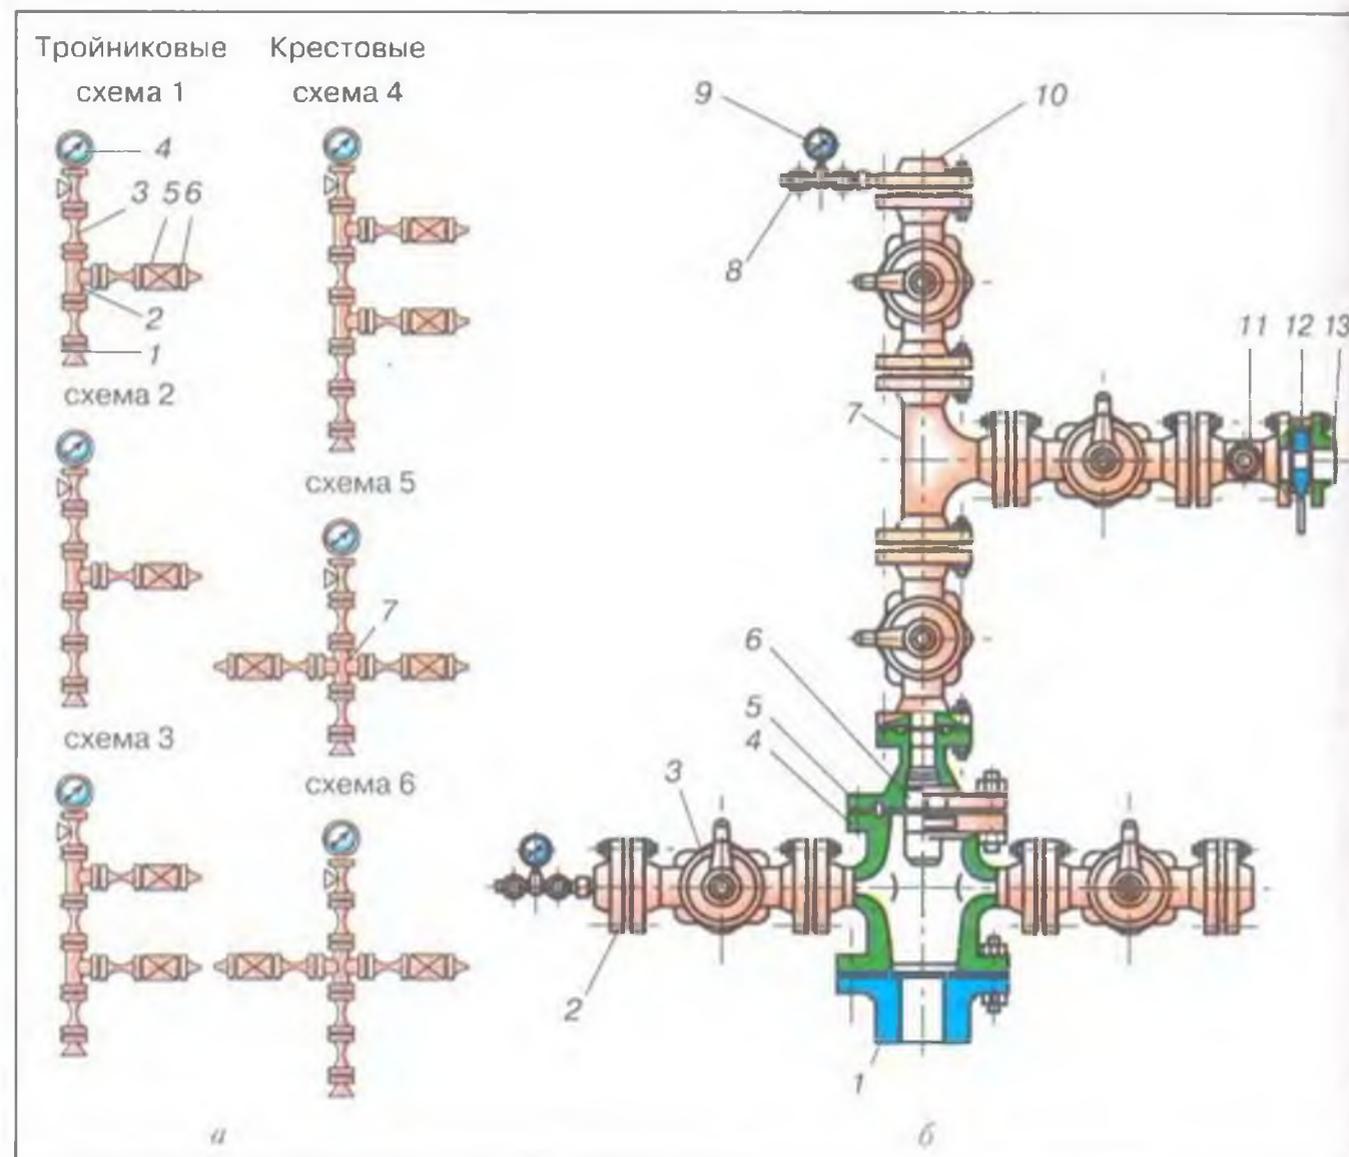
Устьевое оборудование: а – типовые схемы фонтанных елок (1 – переводник к трубной головке; 2 – тройник; 3 – запорное устройство; 4 – манометр с запорно-разрядным устройством; 5 – дроссель; 6 – ответный фланец; 7 – крестовина); б – фонтанная арматура АФК1 – 65 × 14 (1 – колонный фланец; 2 – боковой буфер; 3 – кран; 4 – корпус трубной головки; 5 – стволовая катушка; 6 – патрубок; 7 – тройник; 8 – запорный игольчатый вентиль; 9 – манометр; 10 – верхний буфер; 11 – переводная катушка; 12 – штуцер; 13 – фланец).
